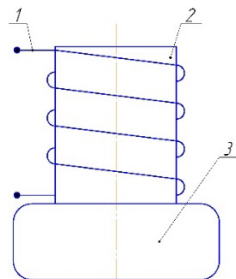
Схема індукційного нагріву робочої зони заготовки при штампуванні обкочуванням:
